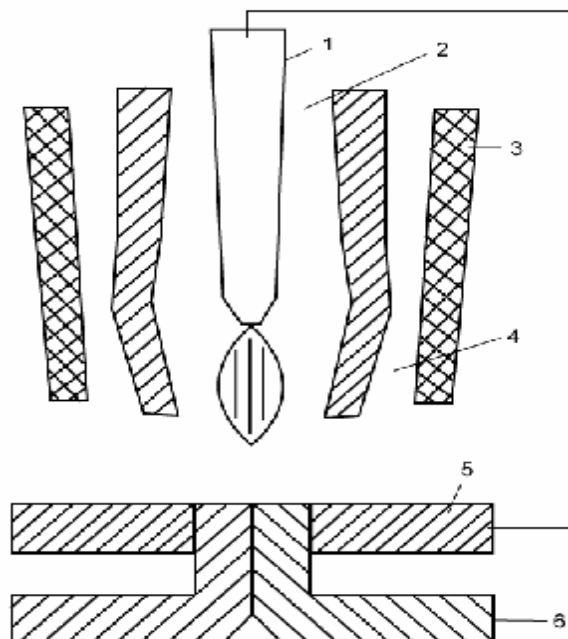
Схема аргонно-дуговой сварки с защитой сварного шва от окисления
